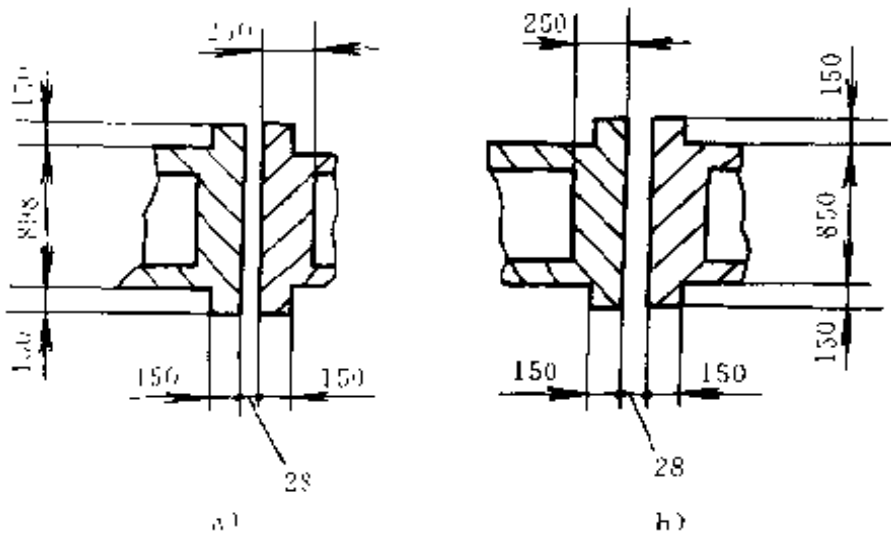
立辊轧机机架的焊接坡口形式及尺寸
